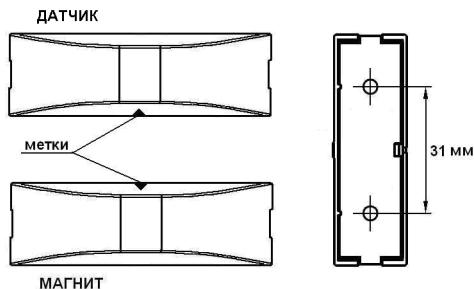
Общий вид и установочный размер датчика и магнита извещателей
